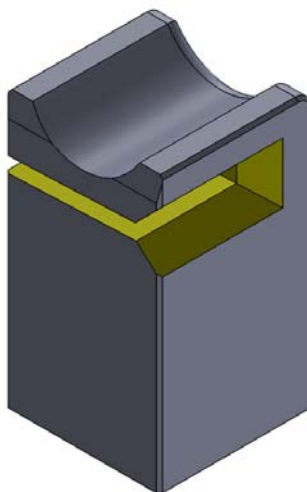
Pormenor da matriz de corte do excesso de bobina
